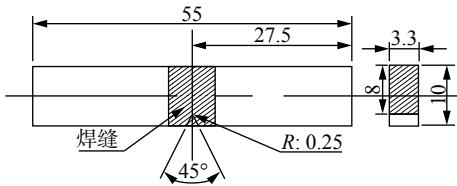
焊缝低温冲击试样取样位置和几何尺寸 (mm)
